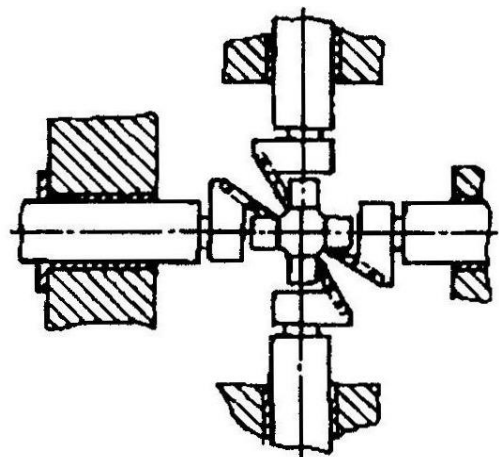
Налаштування агрегатного верстата для обточування цапф хрестовини
